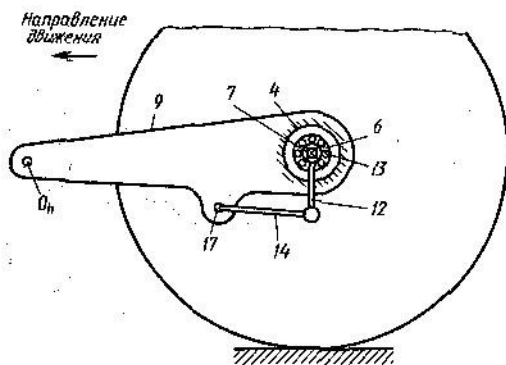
Правый поворотный рычаг 9 (позиции — общие с рис. 3.63), установленный на поворотной опоре, связан через детали 17, 12, 7, 6 и 4 с левым рычагом, чтобы при более мощном двигателе 1,5 л обеспечить требуемую стабилизацию на повороте
